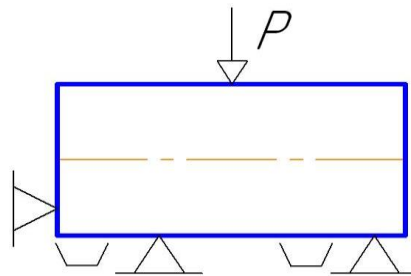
Умовна схема базування при обробці шпонкових пазів на вертикально-фрезерному верстаті
